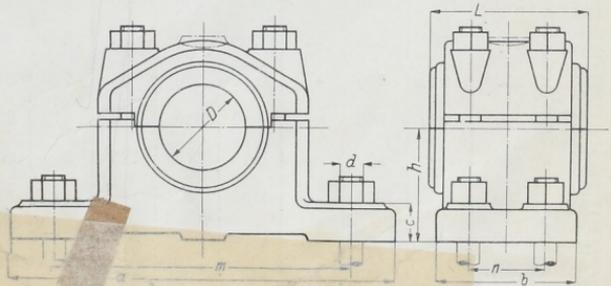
Deckellager mit vier Fußschrauben, nach DIN 506.
